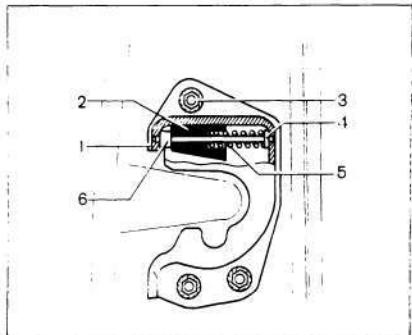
Фиксатор замка двери: 1 — корпус фиксатора; 2 — сухарь; 3 — болт; 4 — ось; 5 — пружина; 6 — втулка
